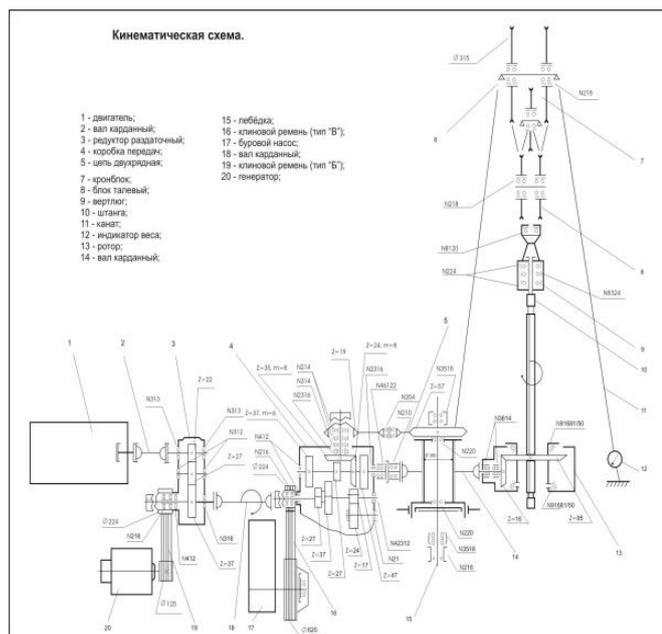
Кинематическая схема буровой установки УРБ-2А-2
